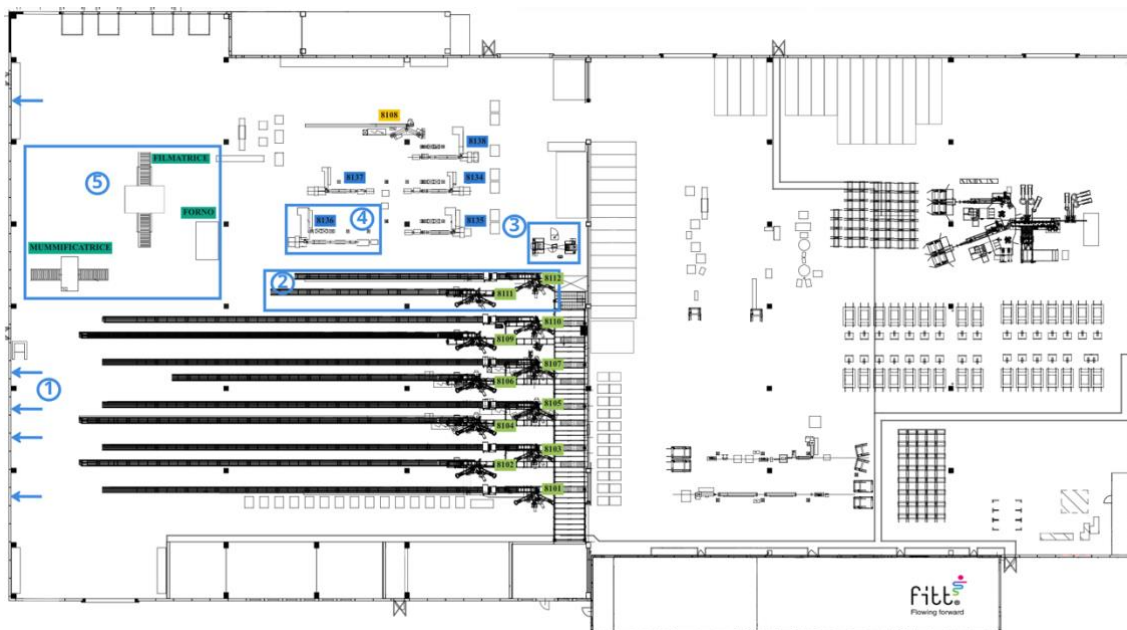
Pianta in scala della prima ipotesi di re-layout (FITT, 2022)
